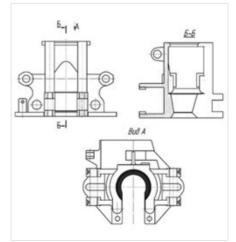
Общий вид корпуса спайдера СПГ-8о (заливкой обозначена изнашиваемая поверхность)
